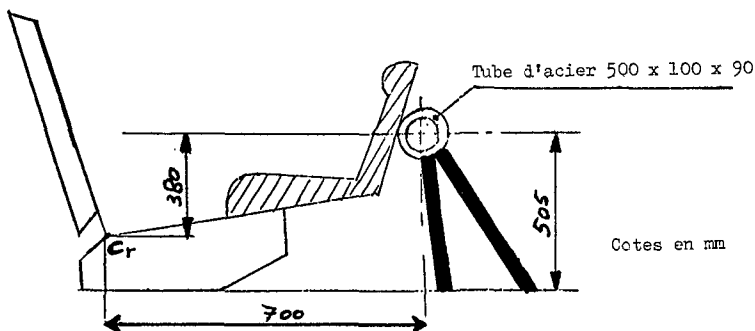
MÉTHODE D'ESSAI D'UN DISPOSITIF FAISANT FACE À L'ARRIÈRE
